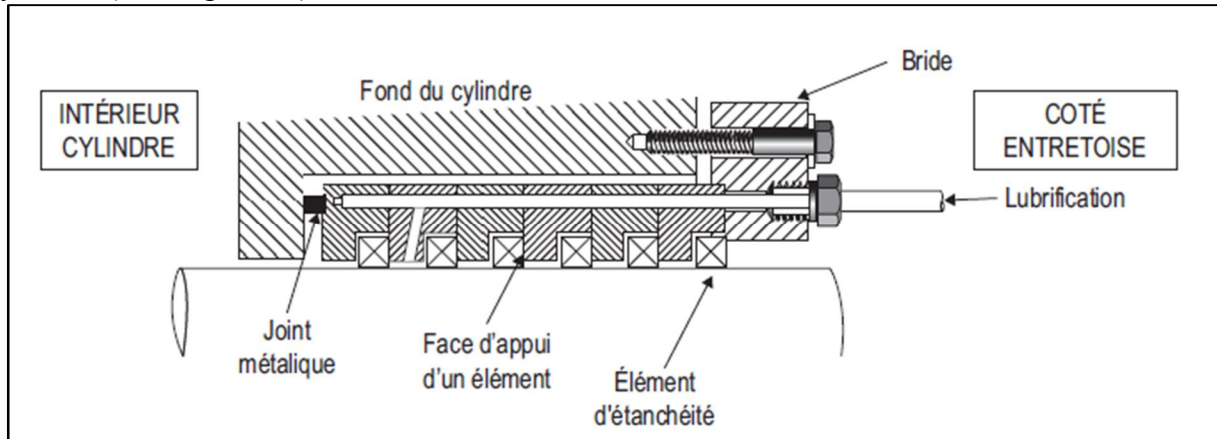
Exemple de montage des cuvettes dans une garniture.
